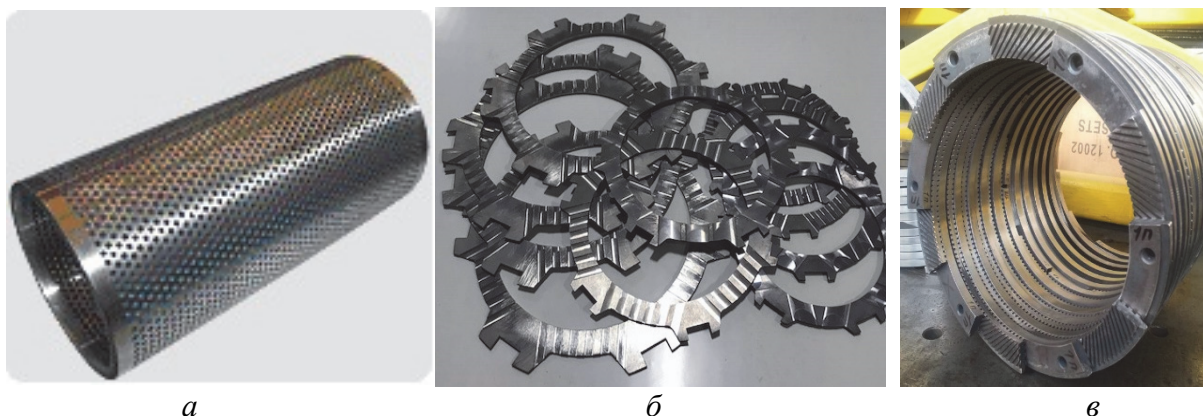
Различное исполнение сепараторов в обвалочных прессах:
